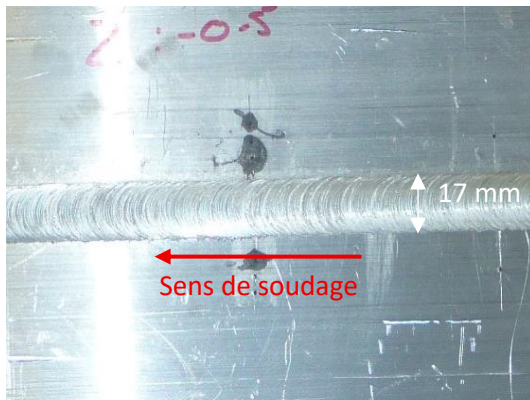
Photographie de la surface supérieure de la soudure T3 (outil B, 800 tr/min, 600 mm/min)
